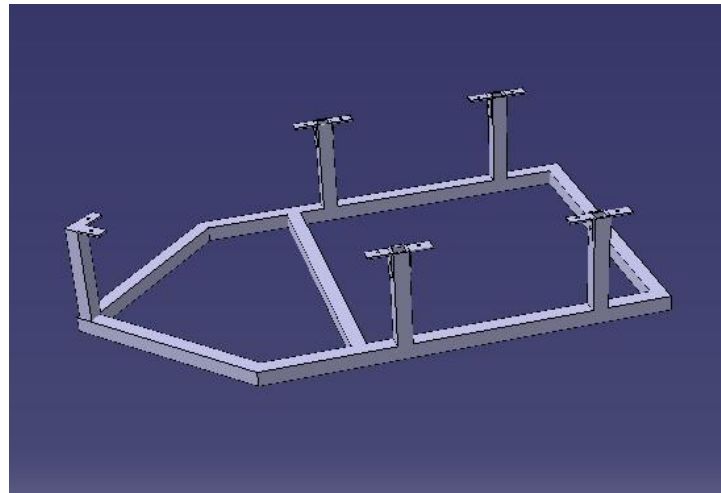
Estrutura em alumínio com ligações soldadas.
